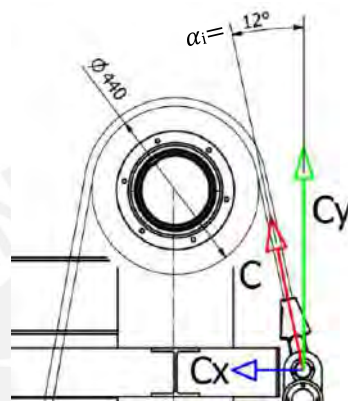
Componentes Horizontal y Vertical de la carga de ensayo C para cable de 22 mm.
